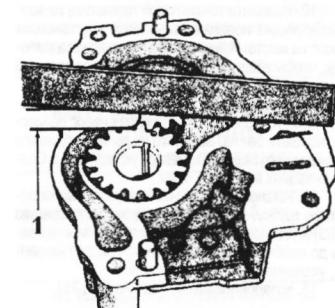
Используйте ровный край и толщиномер для проверки конечного люфта приводной шестерни
